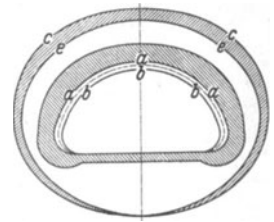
Berücksichtigung der Blechdehnung ermöglicht genauere Zuschnittsberechnung.
